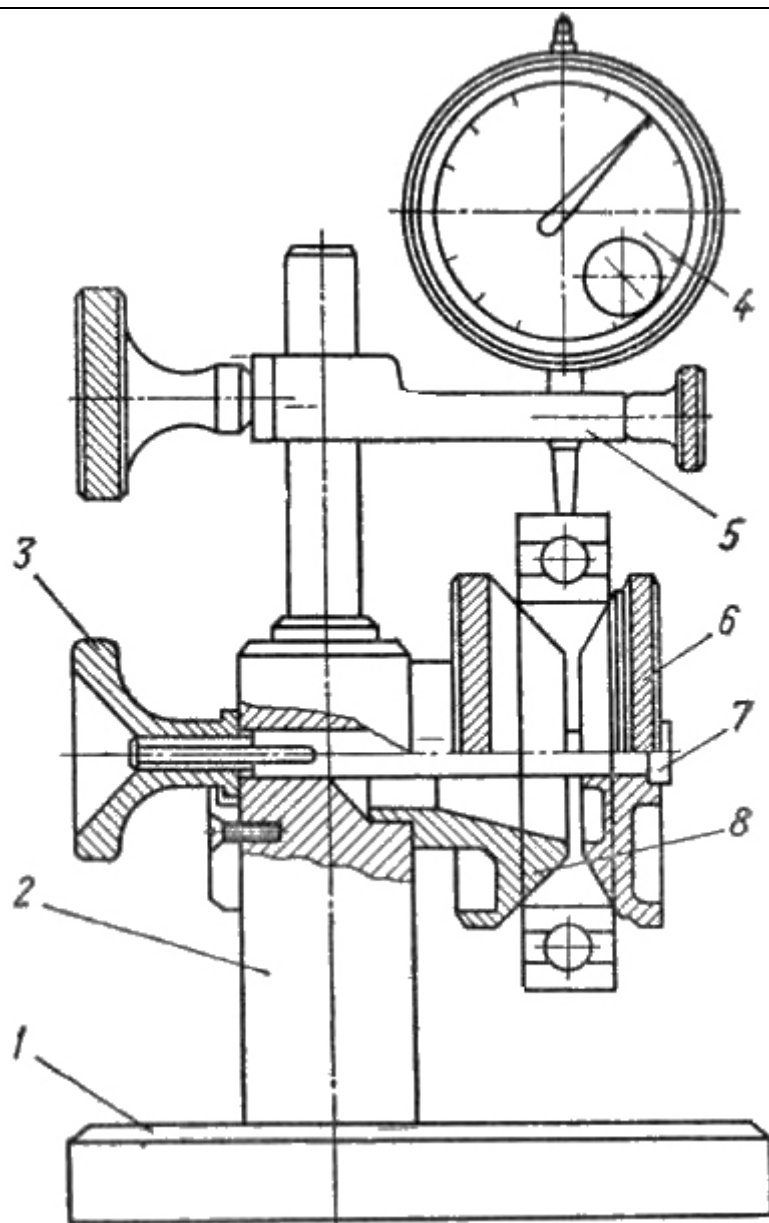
Прибор 1-0942 для измерения радиального зазора подшипников качения.
